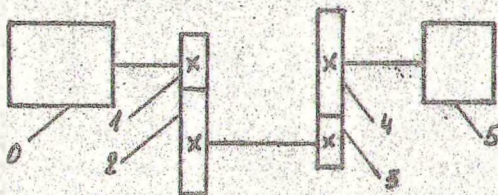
Кинематическая схема привода шпиндельного токарного станка: 0 - ротор двигателя; 1-4 - двухступенчатая цилиндрическая зубчатая передача; 5 - шпиндель
